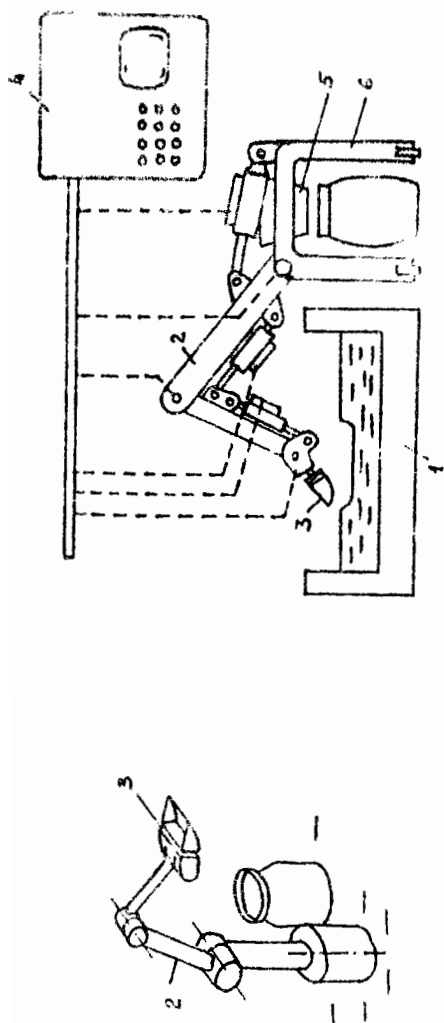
Нутчфильд [42]. 1 - нутч; 2 - коленчатый рычаг; 3 - рычаг; 3 - ковшовый или роторный рабочий орган; 4 - управляющая станция; 5 - воронка; 6 - станция.
